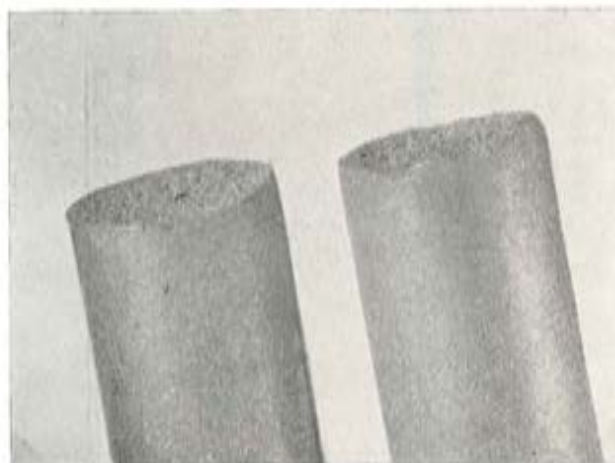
, b. — Templado y revenido. Rotura por fragilización por hidrógeno ($\times 12$).
